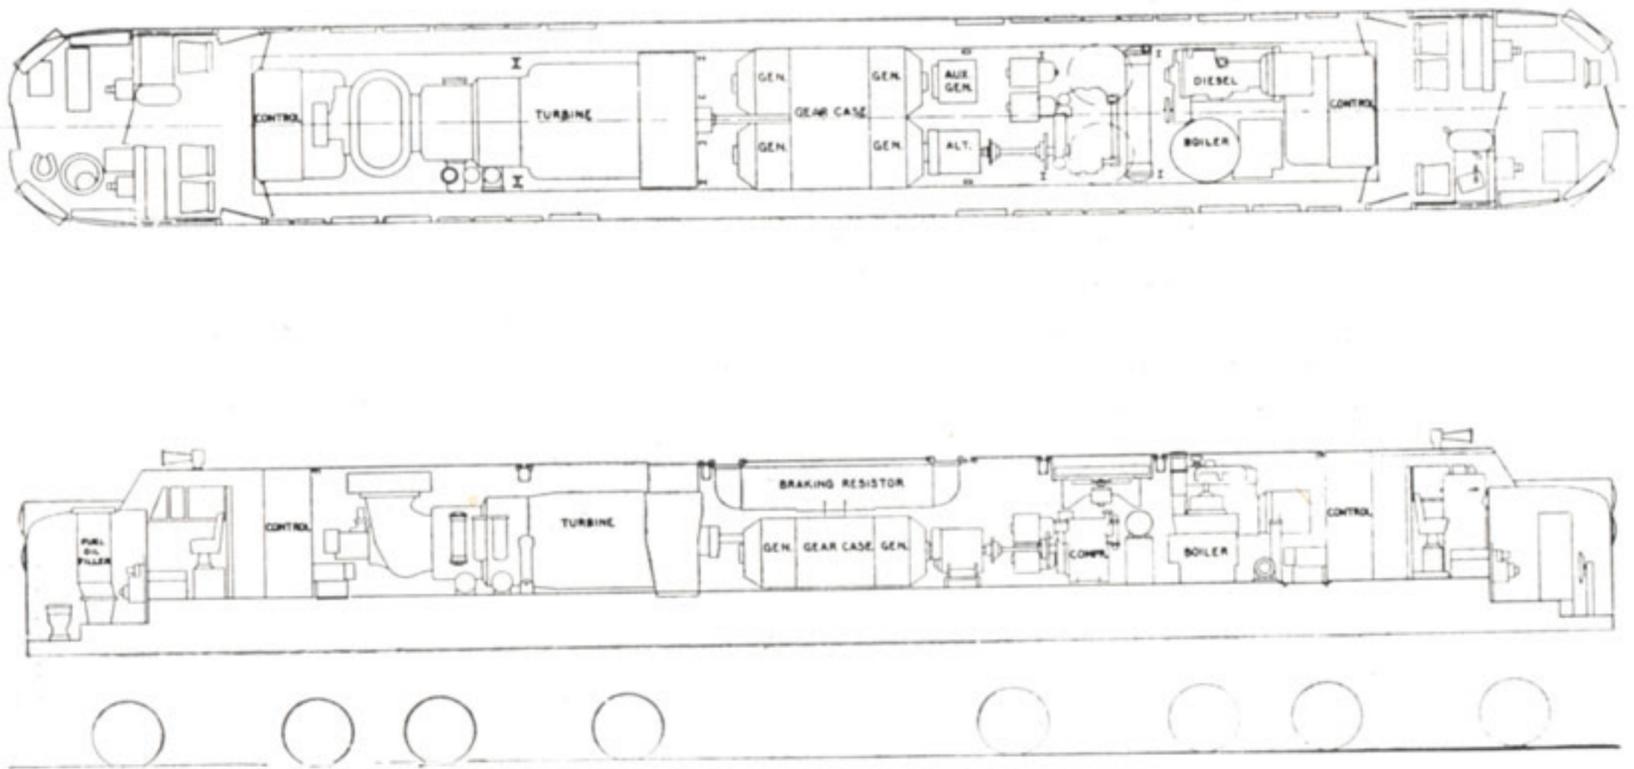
Vue en plan et en élévation de la 101 d'ALCO-GE. — Fuel oil filter = filtre à combustible; control = appareillage; gen = génératrices; gear case = réducteurs à engrenages; braking resistor = résistances du frein rhéostatique; boiler = chaudière de chauffage. A remarquer le réservoir s'étendant sur toute la longueur du véhicule au-dessus du châssis. (Document GE)
